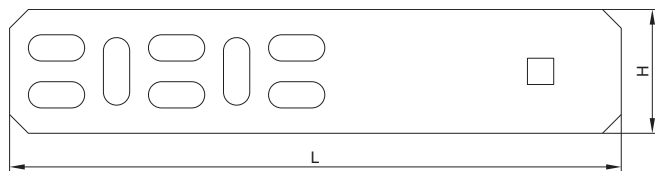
Пластина шарнирного соединения CLP1SH, EALP1SH / Figure D.1 — CLP1SH, EALP1SH hinge joint plate
